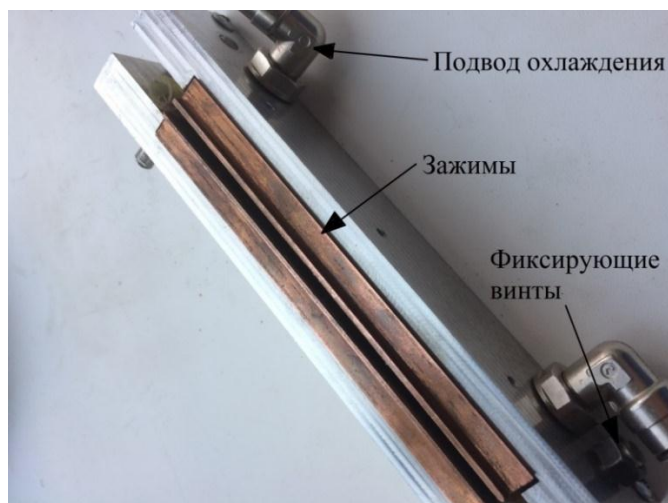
Оснастка для сварки конверта теплообменника
